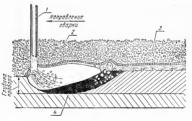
Схема образования сварочного шва под флюсом: 1 — электрод; 2 — флюсовый пузырь; 3 — слой флюса; 4 — ванна жидного мегалла.
